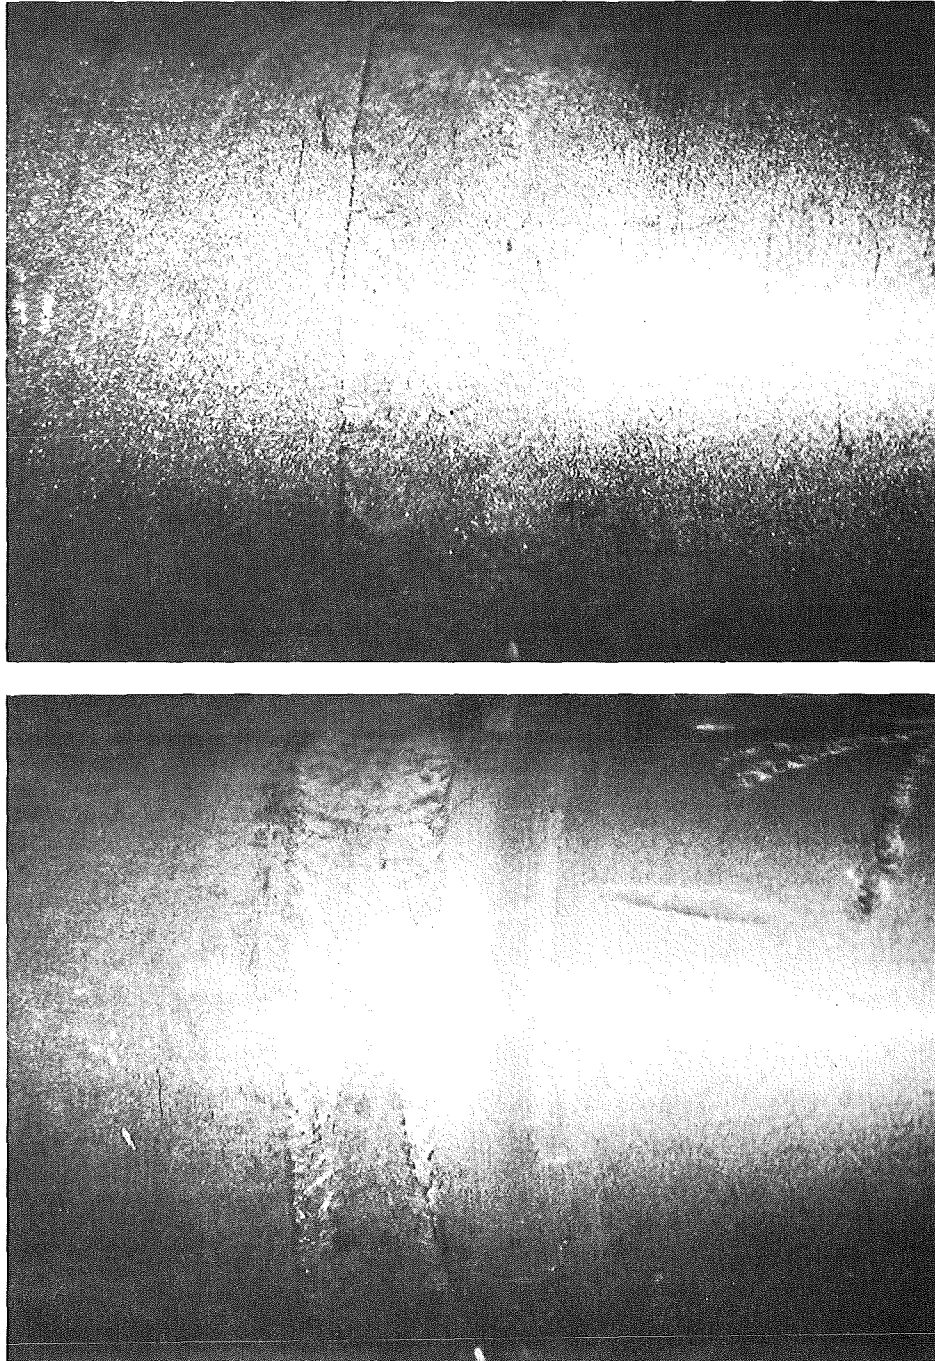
Auflichtaufnahmen von Schweißnähten mit dem OP-Mikroskop, Beispiele typisch für alle Proben
